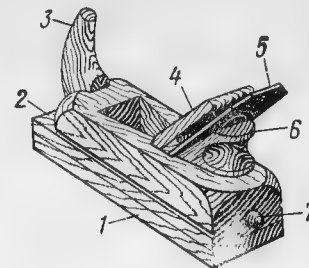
1 — подошва; 2 — корпус; 3 — рог; 4 — клин; 5 — нож; 6 — упор; 7 — пробка
